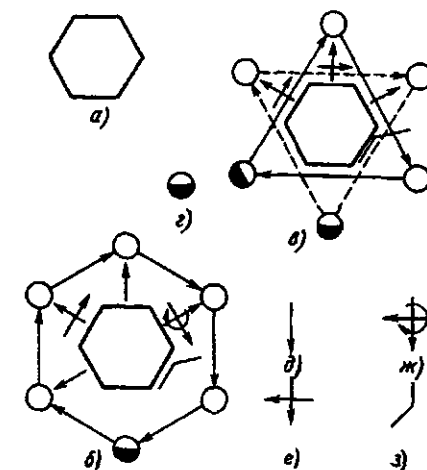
Схемы наладки полуавтоматов и условные обозначения позиций и движения суппортов: а – колонка станка; б – схема одноциклового наладки станка; в – схема двухциклового наладки станка; г – загрузочная позиция; д – вертикальный суппорт; е – горизонтальный (полууниверсальный) суппорт; ж – универсальный суппорт; з – сдвоенный угловой суппорт
